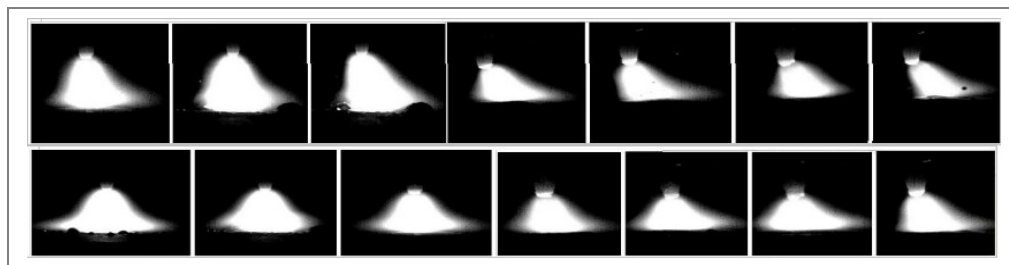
Видеокадры сварочной дуги при аргонодуговой сварке промышленной (вверху) и разработанной (внизу) горелкой. Слева-направо: скорость ветра 2,5; 2,8; 3,5; 4,8; 5,8; 6,3 м/с
